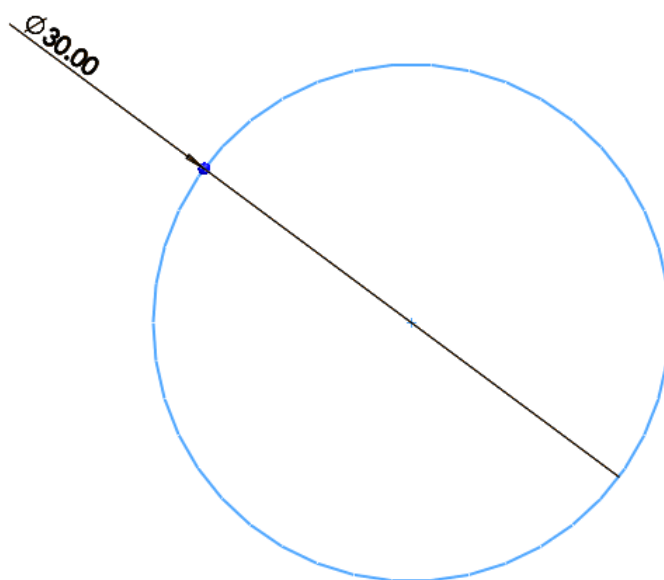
Эскиз детали 8: гайка шпильки.
